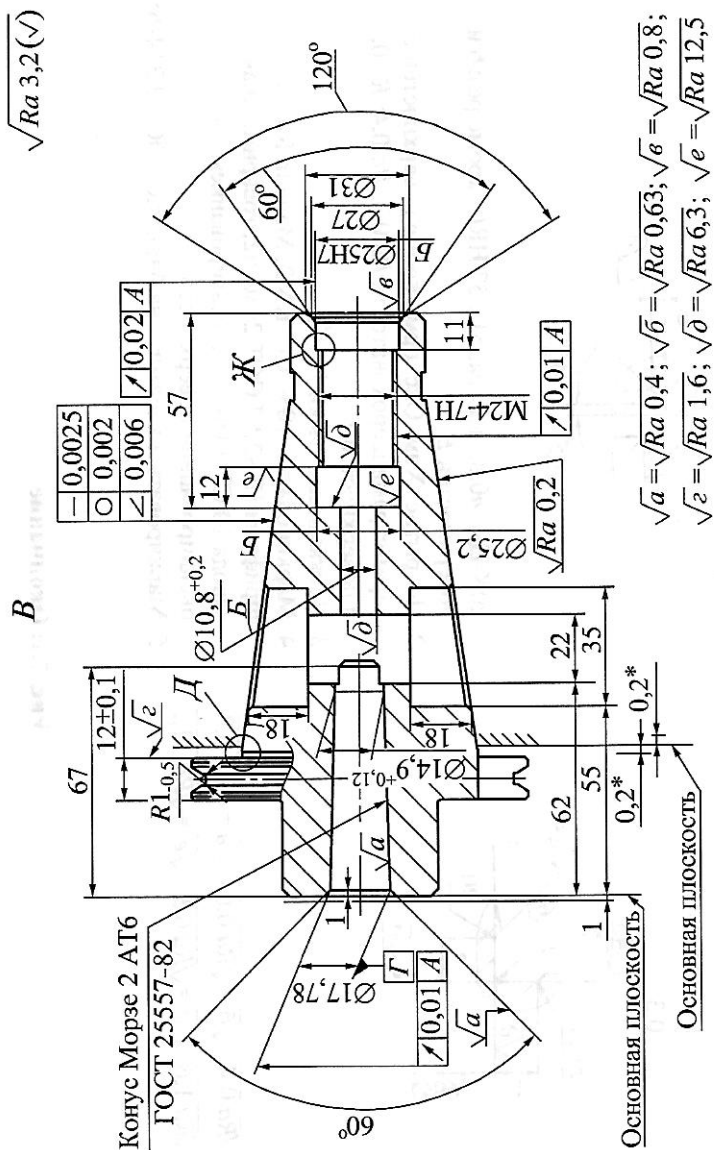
Рабочий чертеж корпуса ВИ с конусом 7:24 (начало)
